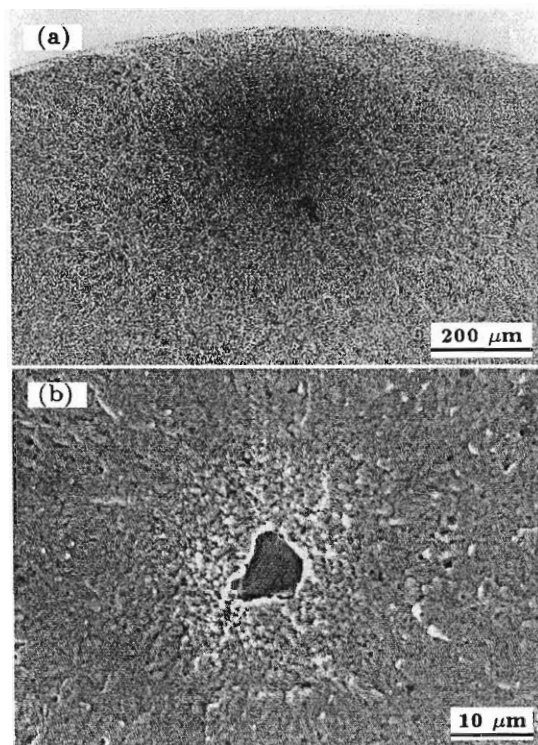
深层滚压试样内部裂纹萌生位置的断口形貌
